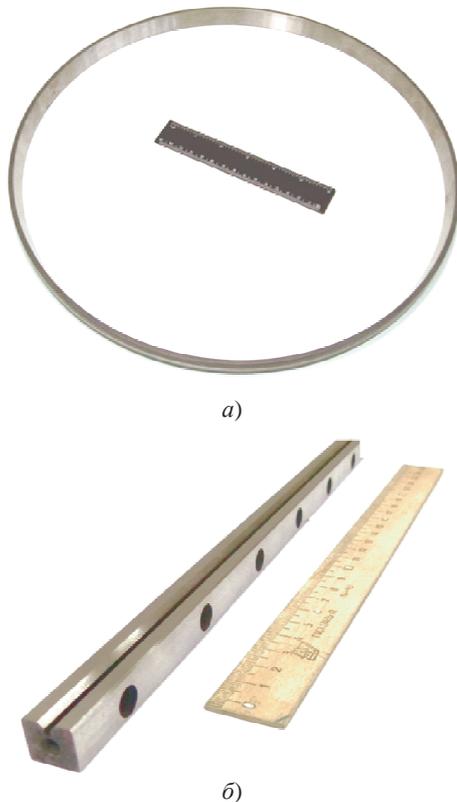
Образцы нежестких заготовок наружного кольца У-7866А.01 роликоподшипника (а) и направляющей (б)
